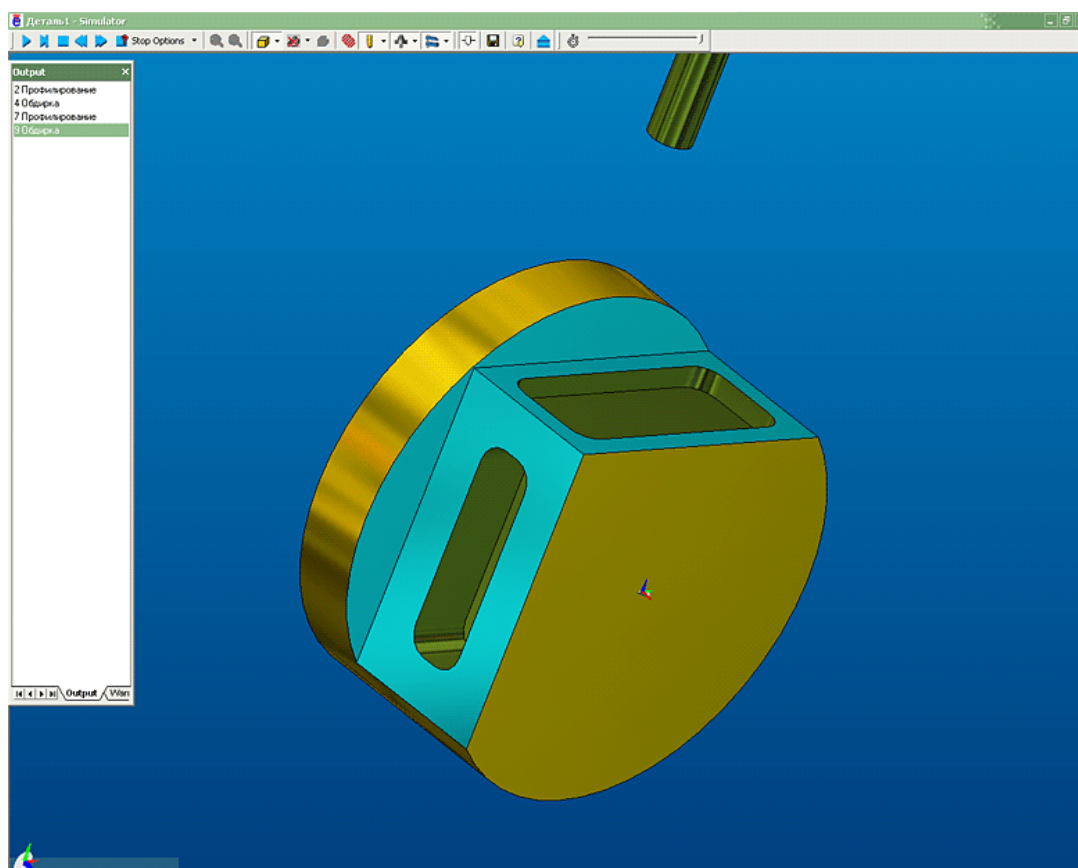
Edgesat. Обработка детали с использованием 4-ой оси.
